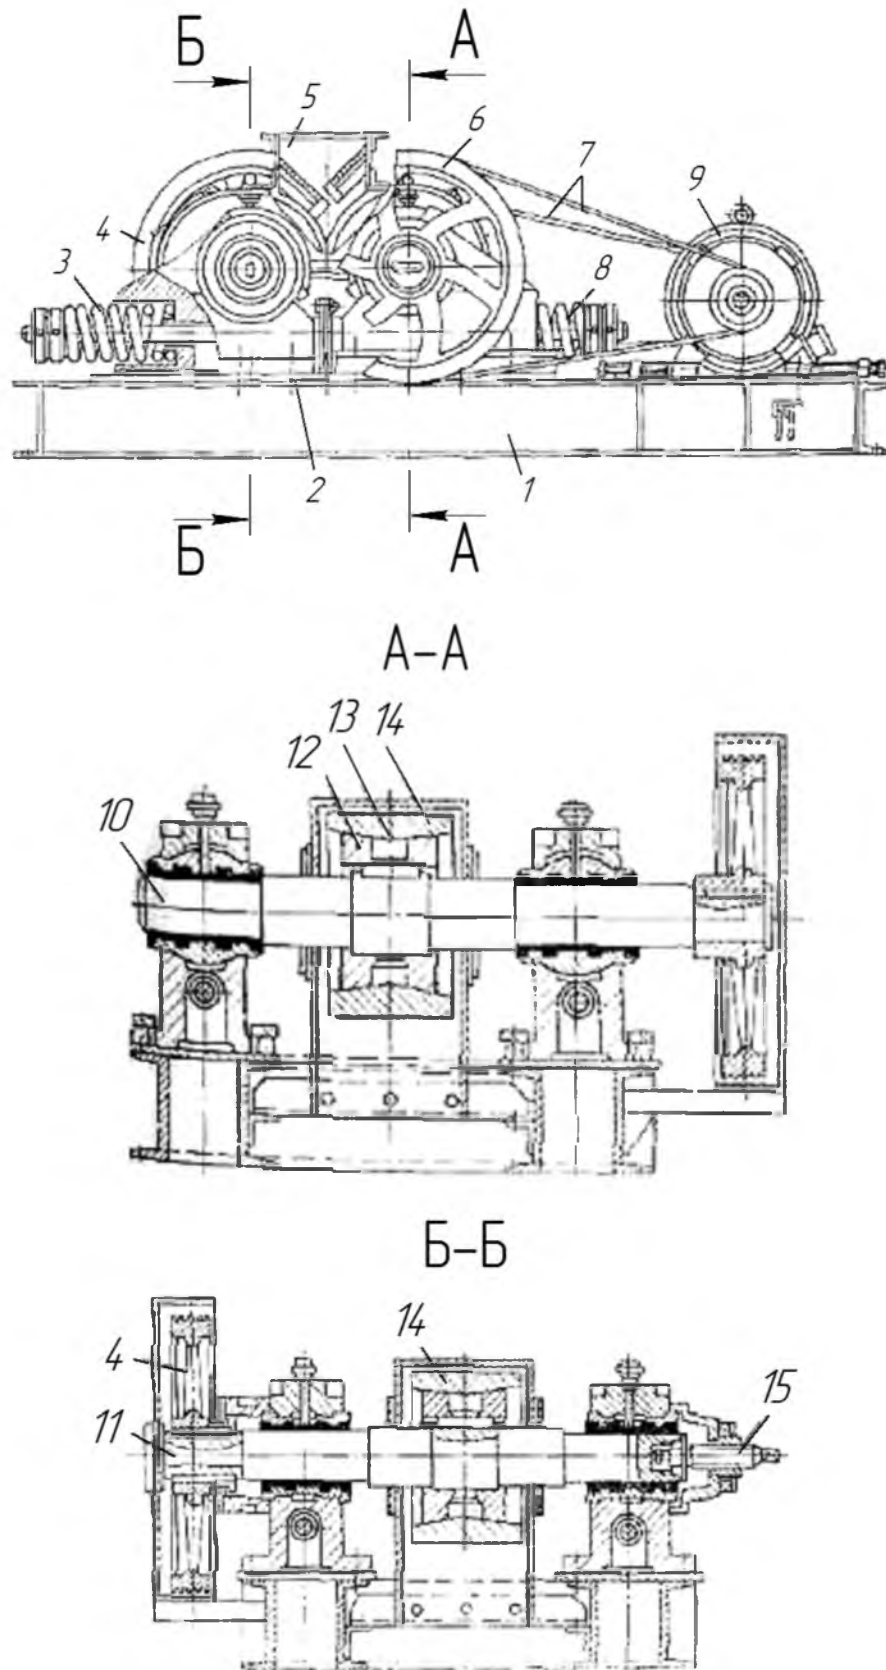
Конструкція двохвалкової дробарки ДГ400×250
